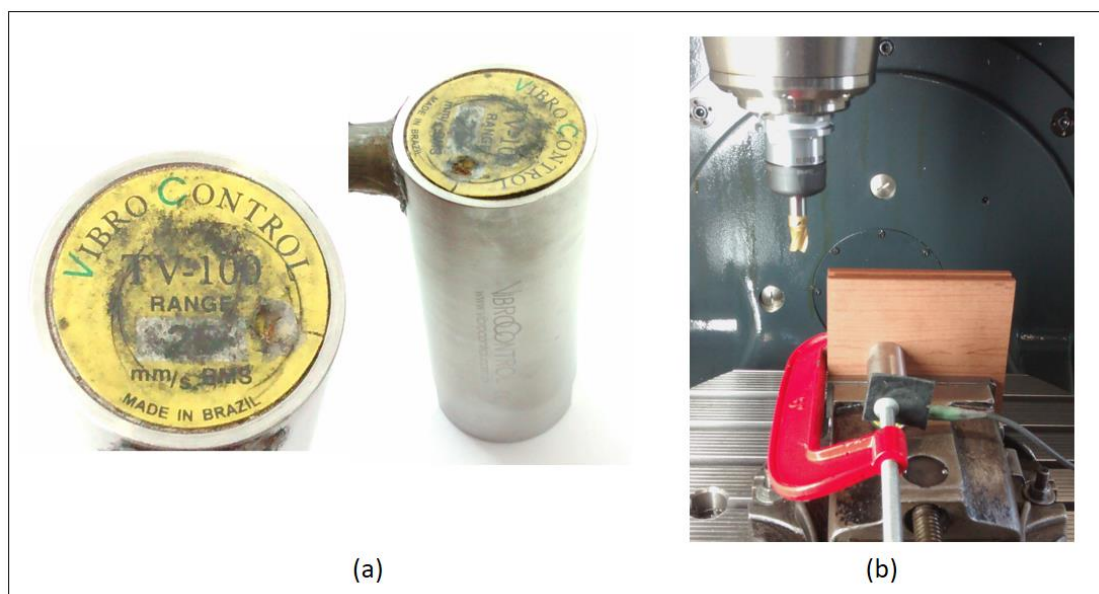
(a) Sensor piezelétrico, marca Vibro Control e (b) acoplamento do sensor para usinagem
